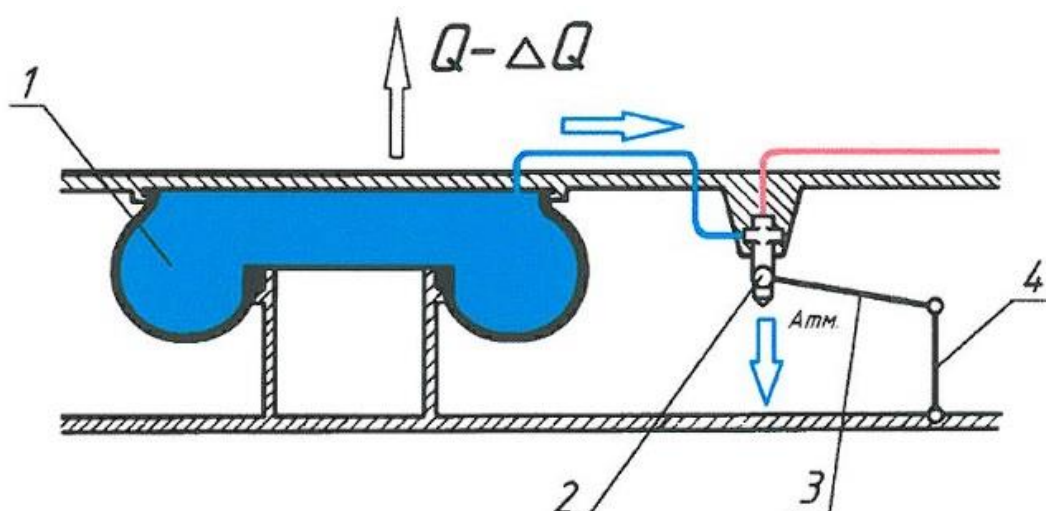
Система пневматической рессоры в положении сброса воздуха:
